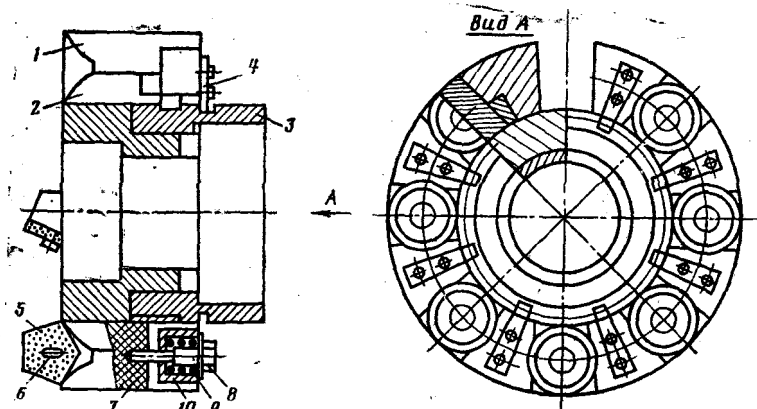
Торцевая фреза с твердосплавными многогранными пластинами для термофрезерования наплавленного металла при совмещенной комплексно-механизированной технологии восстановления деталей: 1 — корпус; 2 — установочная опора; 3 — регулировочная втулка; 4 — стопорная пластина; 5 — твердосплавная многогранная пластина; 6 — штифт; 7 — державка; 8 — болт; 9 — пружинная пластина; 10 — опорное кольцо
